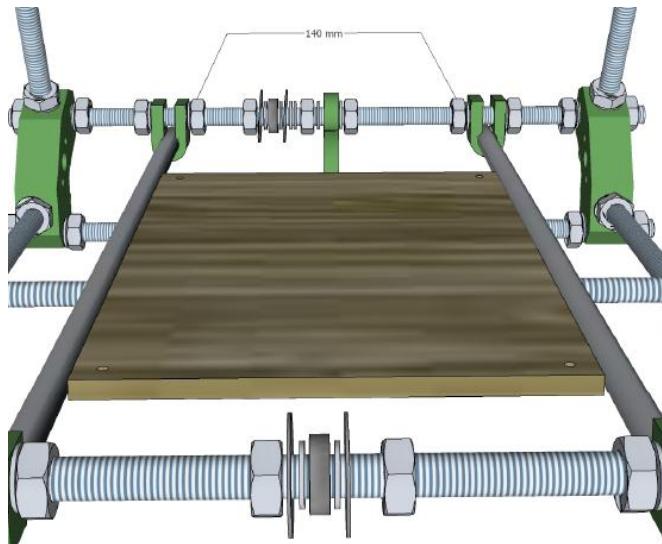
Colocación de varillas transversales y base de madera (paso 4)
